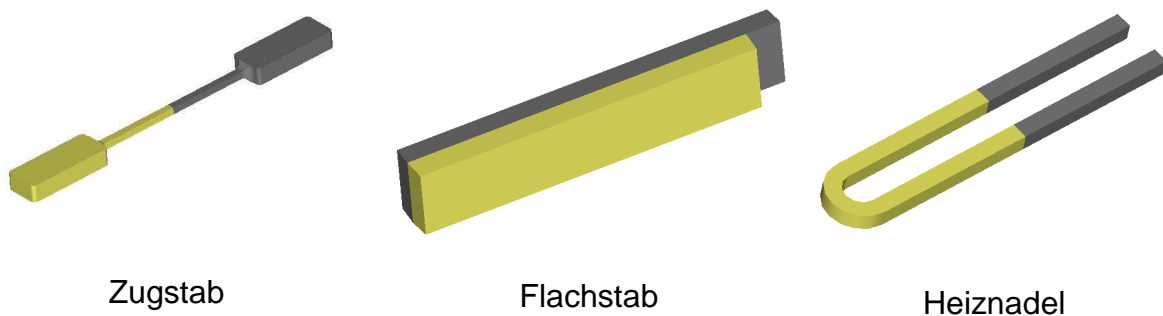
Design der 2K-Probekörper und des Demonstrators
